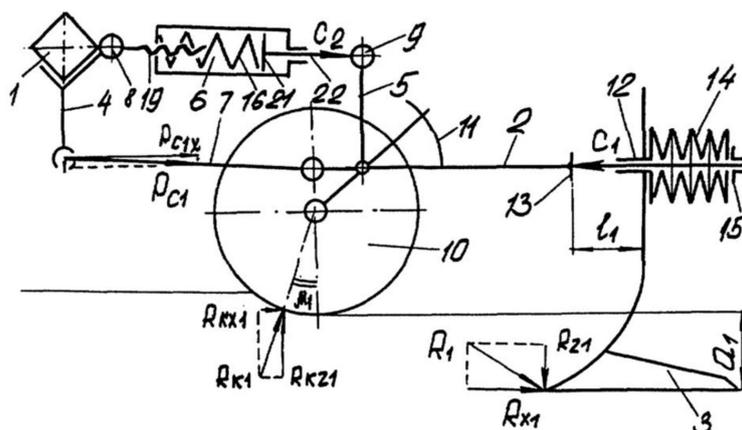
Культиватор-растениепитатель: 1 – брус-рама; 2 – штанга; 3 – рабочие органы; 4 – кронштейн понизителя; 5 – подколесная стойка; 6 – упругое звено; 7 – нижняя тяга; 8 – вал качалок; 9 – вертикальные пазы; 10 – опорное колесо; 11 – механизм; 13 – упор; 14 – тарельчатые пружины; 15 – упорная гайка; 16 – упругий элемент; 17 – стяжная гайка; 18 – резьбовая часть; 19 – поводок; 20 – резьбовая крышка; 21 – подвижный упор; 22 – шток
